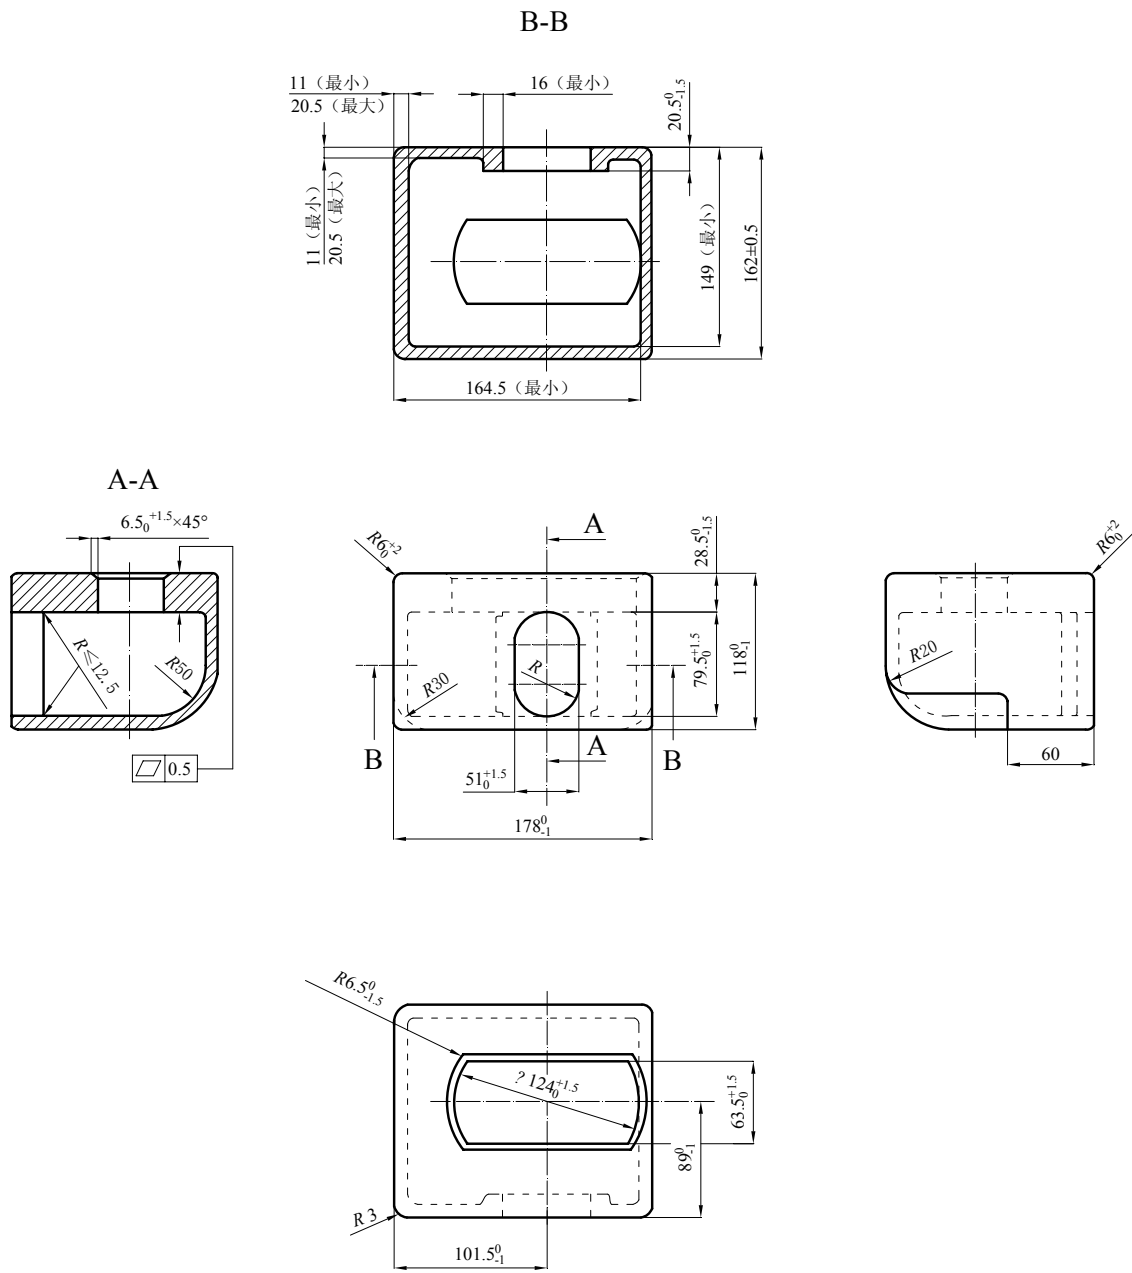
(3) 中间顶角件尺寸 (单位: mm)
